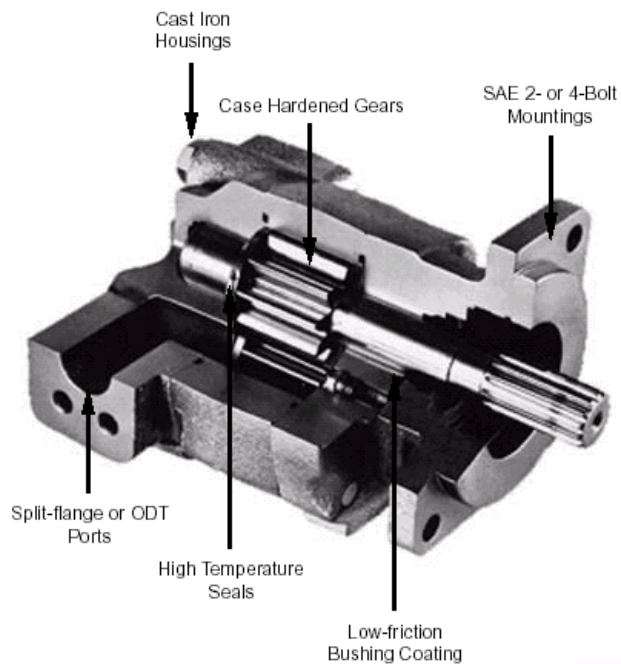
Motor hidráulico de engrenagens, Série PL Factor
